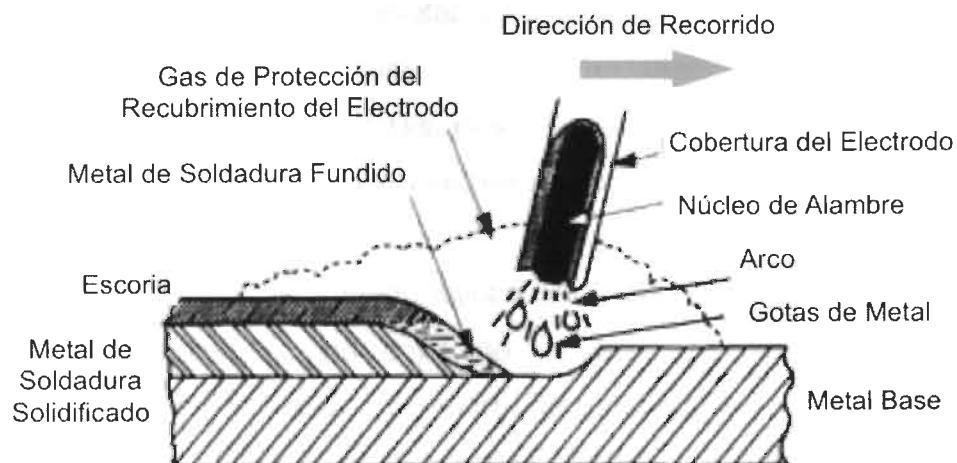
Proceso de Soldadura SMAW.[1]
